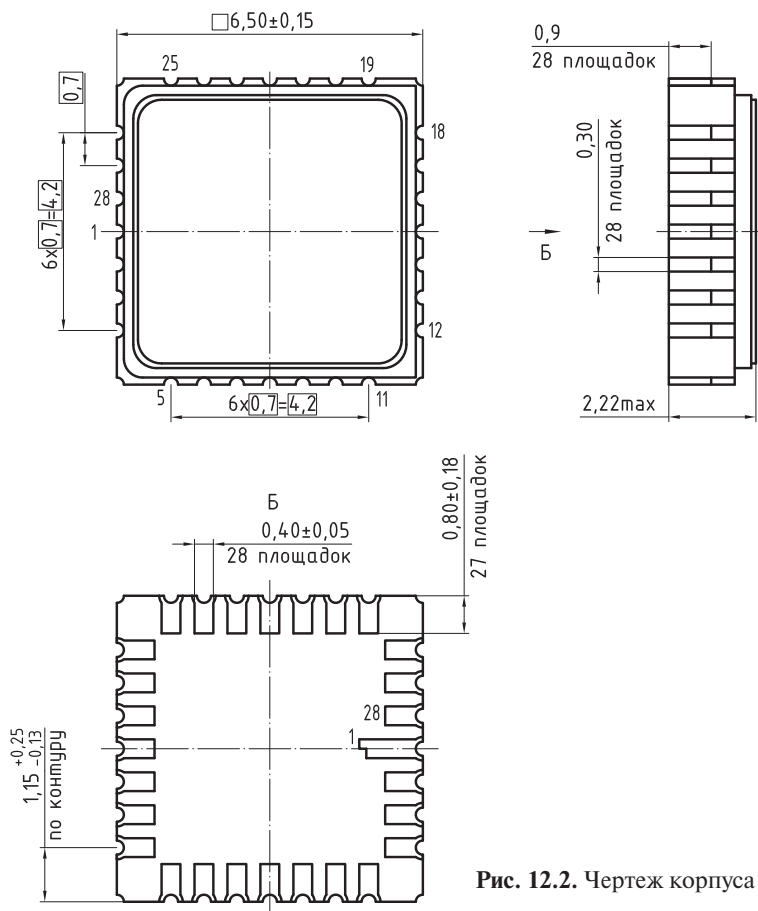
Чертеж корпуса МК 5123.28-1.01
